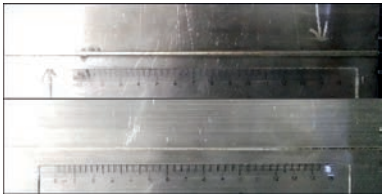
Внешний вид пластин стали SUS304 (δ = 3,0 мм), сваренных встык с зазором 0,5 мм между кромками лазерно-микроплазменным способом (мощность излучения  $P = 1,2$  кВт, сварочный ток  $I = 80$  А, напряжение  $U = 28$  В, скорость сварки  $v = 30$  м/ч): лицевая (а) и обратная (б) стороны
